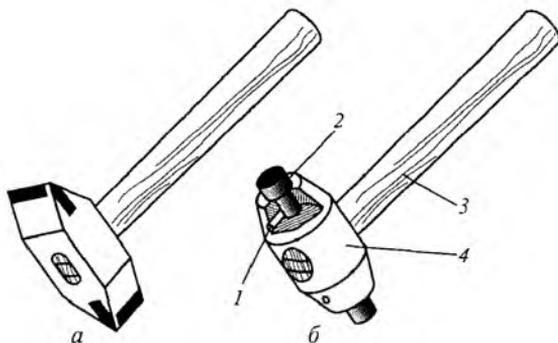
Молотки с мягкими вставками: а – с призматической; б – с цилиндрической: 1 – штифт; 2 – боек; 3 – рукоятка; 4 – корпус
